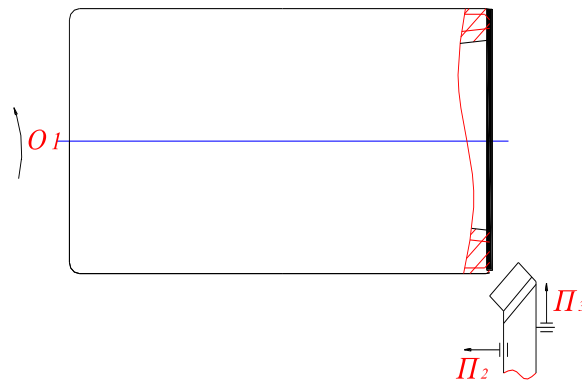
Формоутворення плоскої поверхні (підрізання торця)
